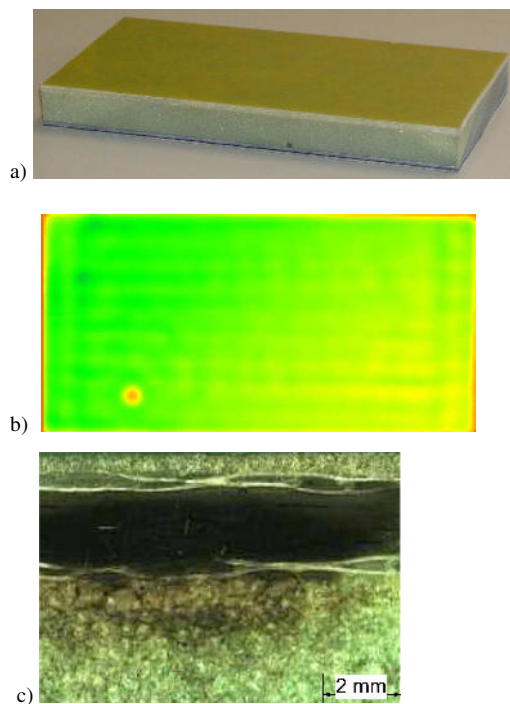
Sandwich GFK/ PVC-Schaum/ CFK mit Defekt: unzureichend harz-getränkte Glasfaserbündel. a) Foto des Sandwich. b) Mikrowellen-C-Scan des Sandwich. c) Schnitt durch Defektregion
